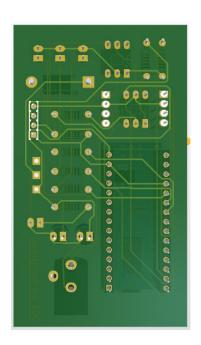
Ảnh đi dây PCB của lớp top và bottom
